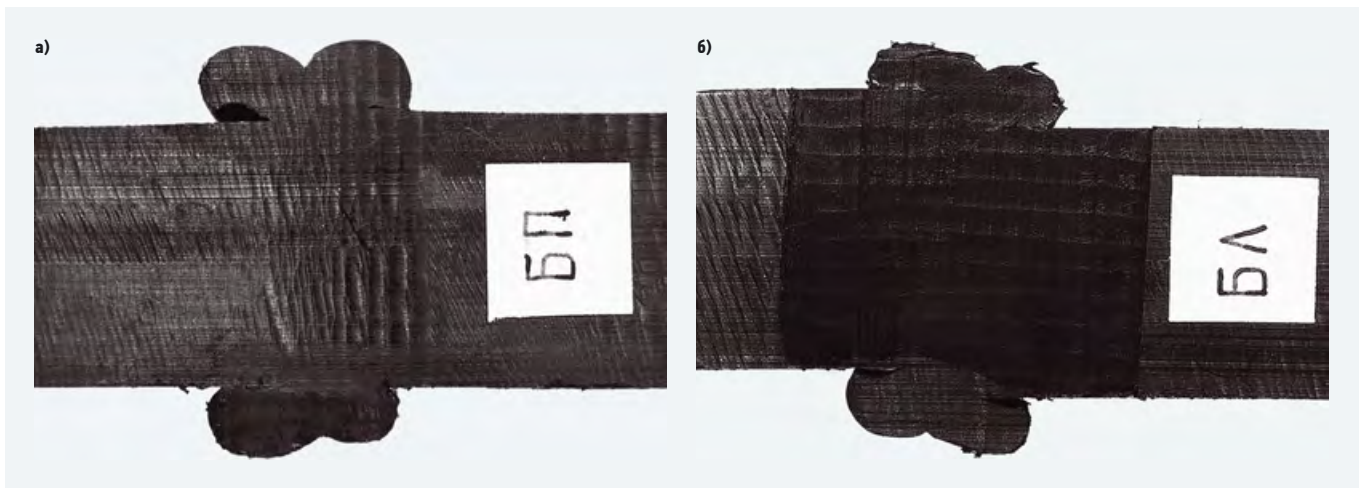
Сварной шов образцов [а — с галтелями, б — с радиальной выточкой; БП, БЛ — вырезка из трубного стыка по диаметру (справа) и относительно сварочного приспособления (слева)]
